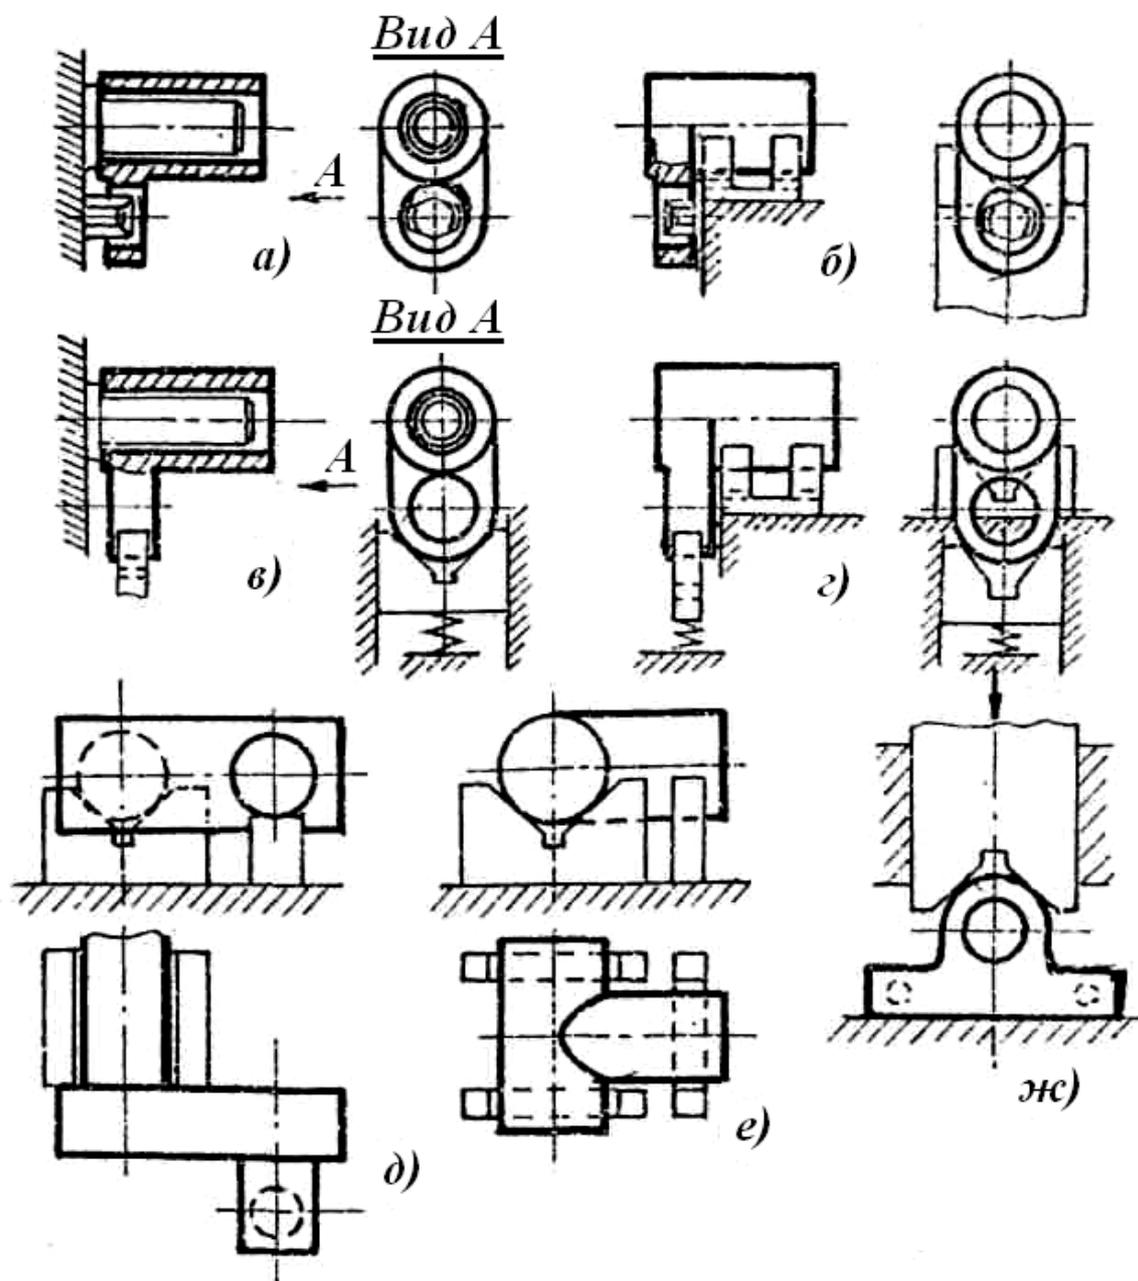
Схемы установки заготовок на цилиндрические и плоские поверхности:
